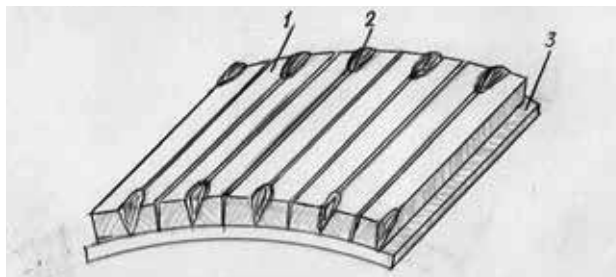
Схема сборки и плазменной сварки стержней
